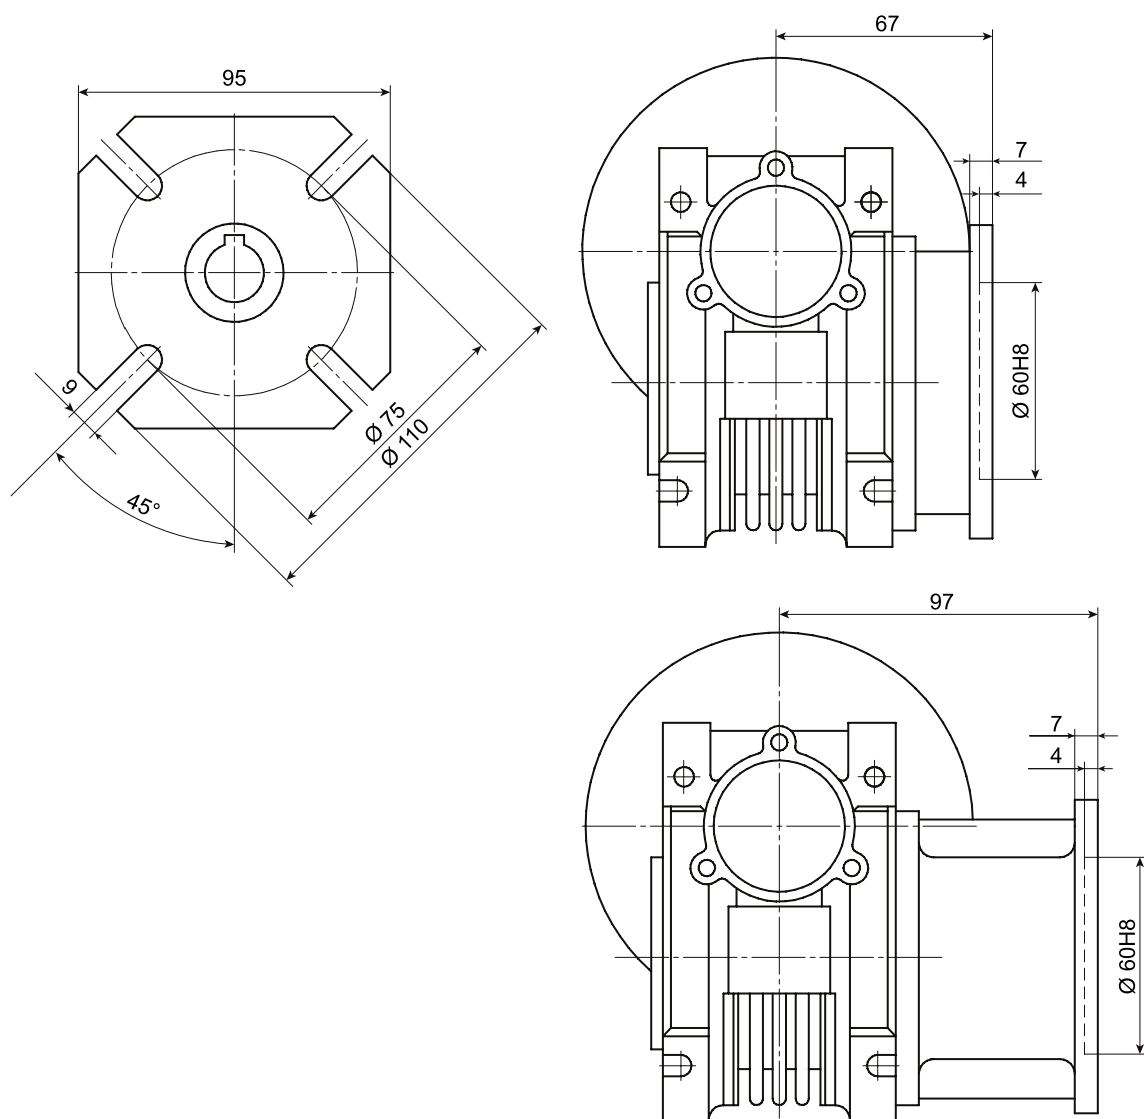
Габаритные размеры боковых фланцев FA и FB
